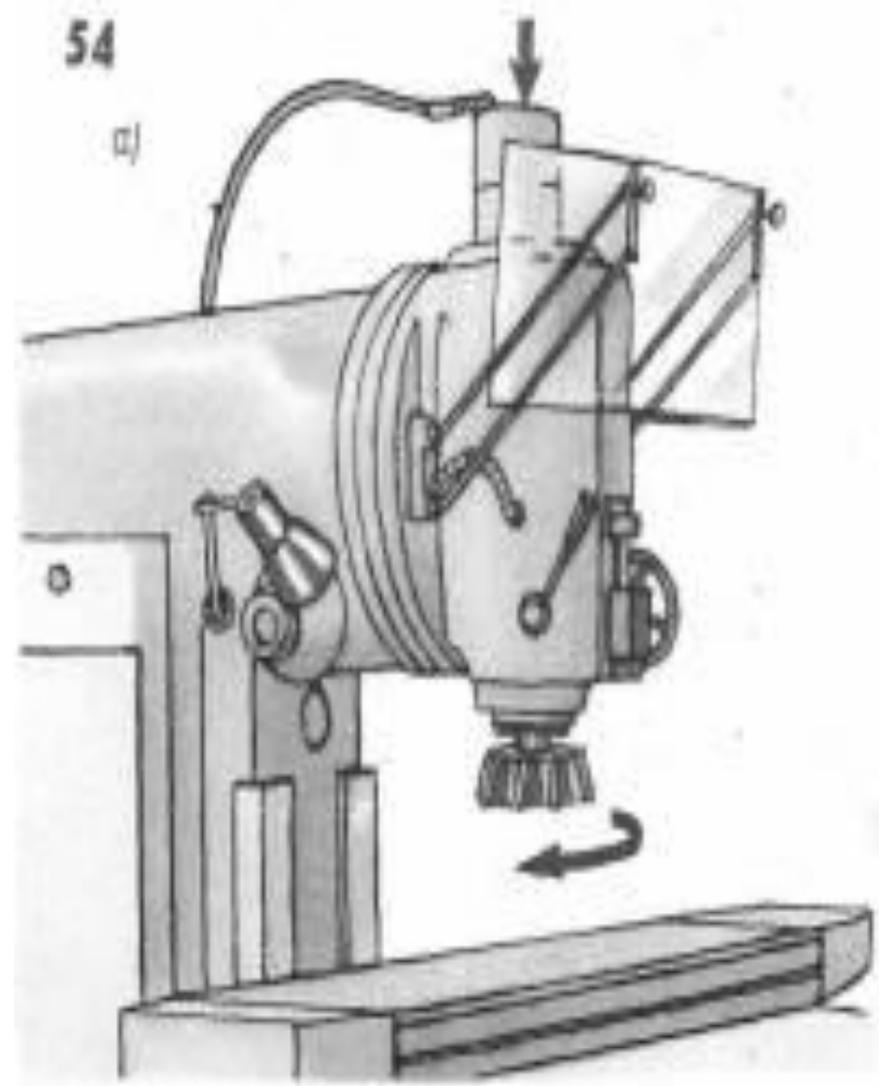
Фрезерование фасонной поверхности [autowelding.ru](http://autowelding.ru)
